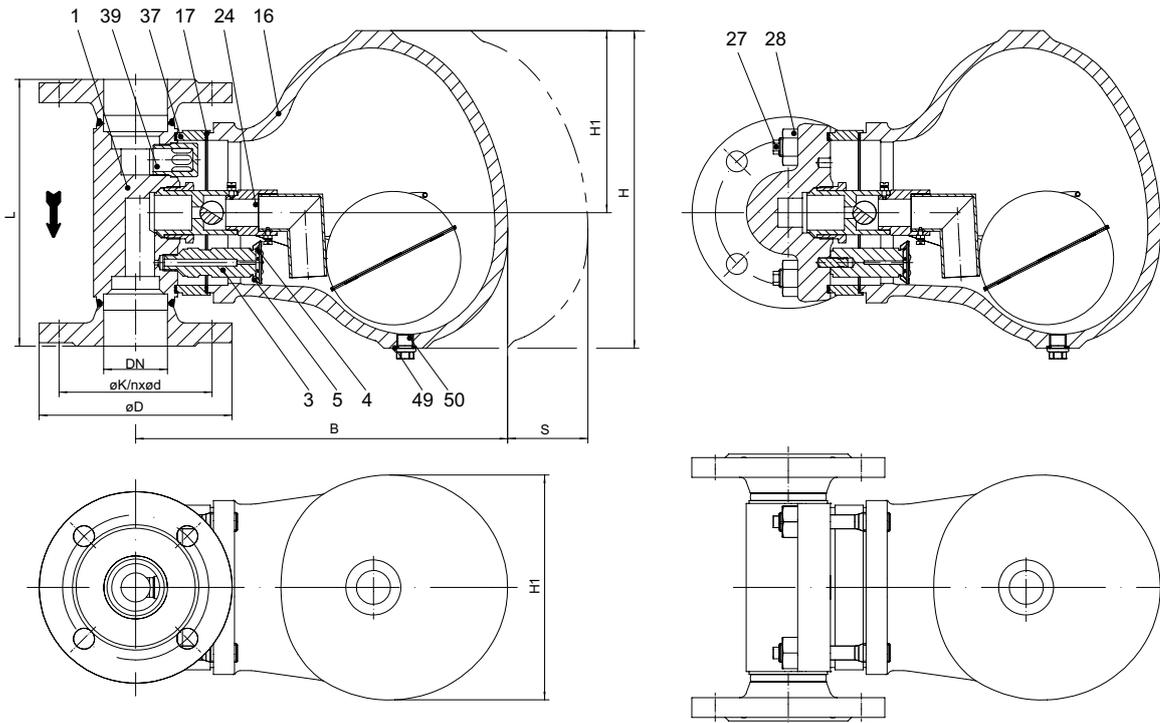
1 mit Flanschen - vertikale Einbaulage
